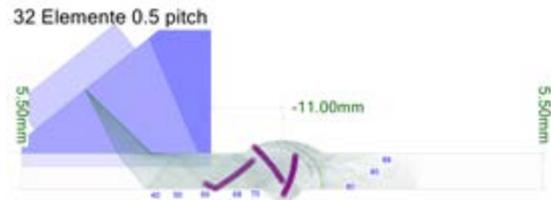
c. LOW-Profile-PAUT-Prüfkopf (16 mm Aperturlänge) auf 5,5 mm Wanddicke
